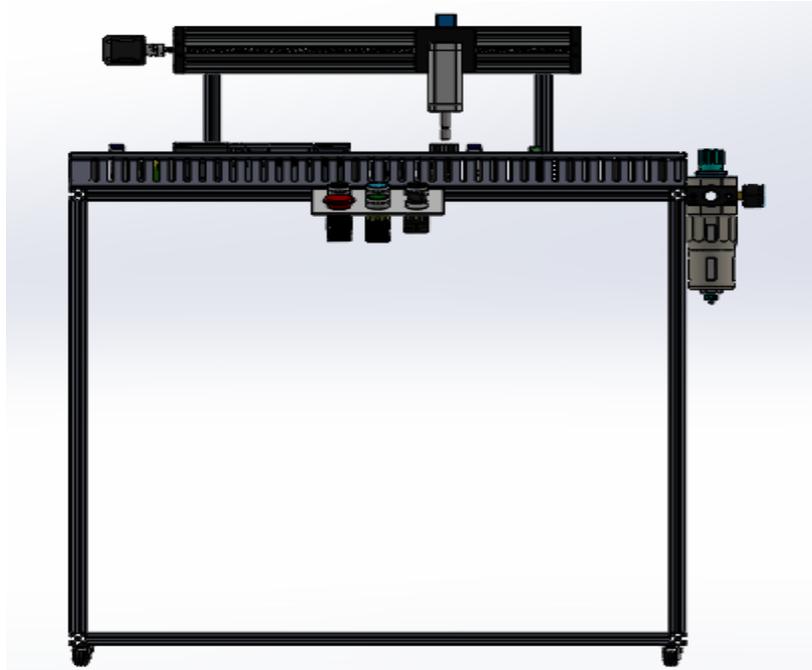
Diseño celda de manufactura flexible, Vista frontal (propia autoría).
